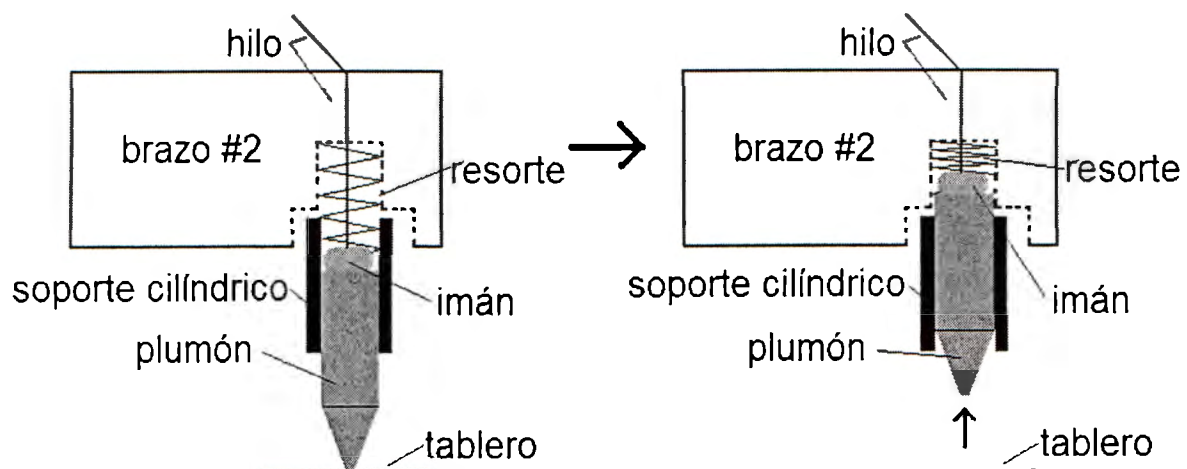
Se observa el plumón en posición baja presionado por el resorte hacia el tablero (izquierda). El servo #3 gira, jala el hilo y hace que el plumón se levante del tablero (derecha).
